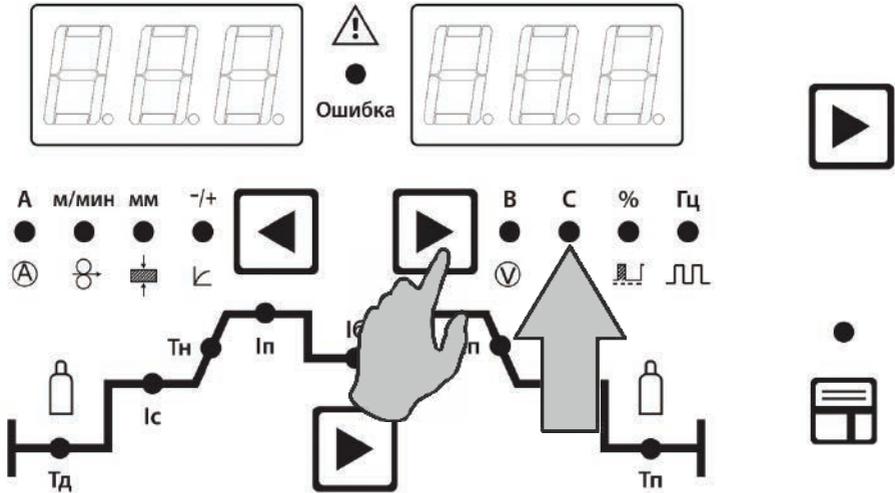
Установка стартового сварочного тока и напряжения на дуге.
